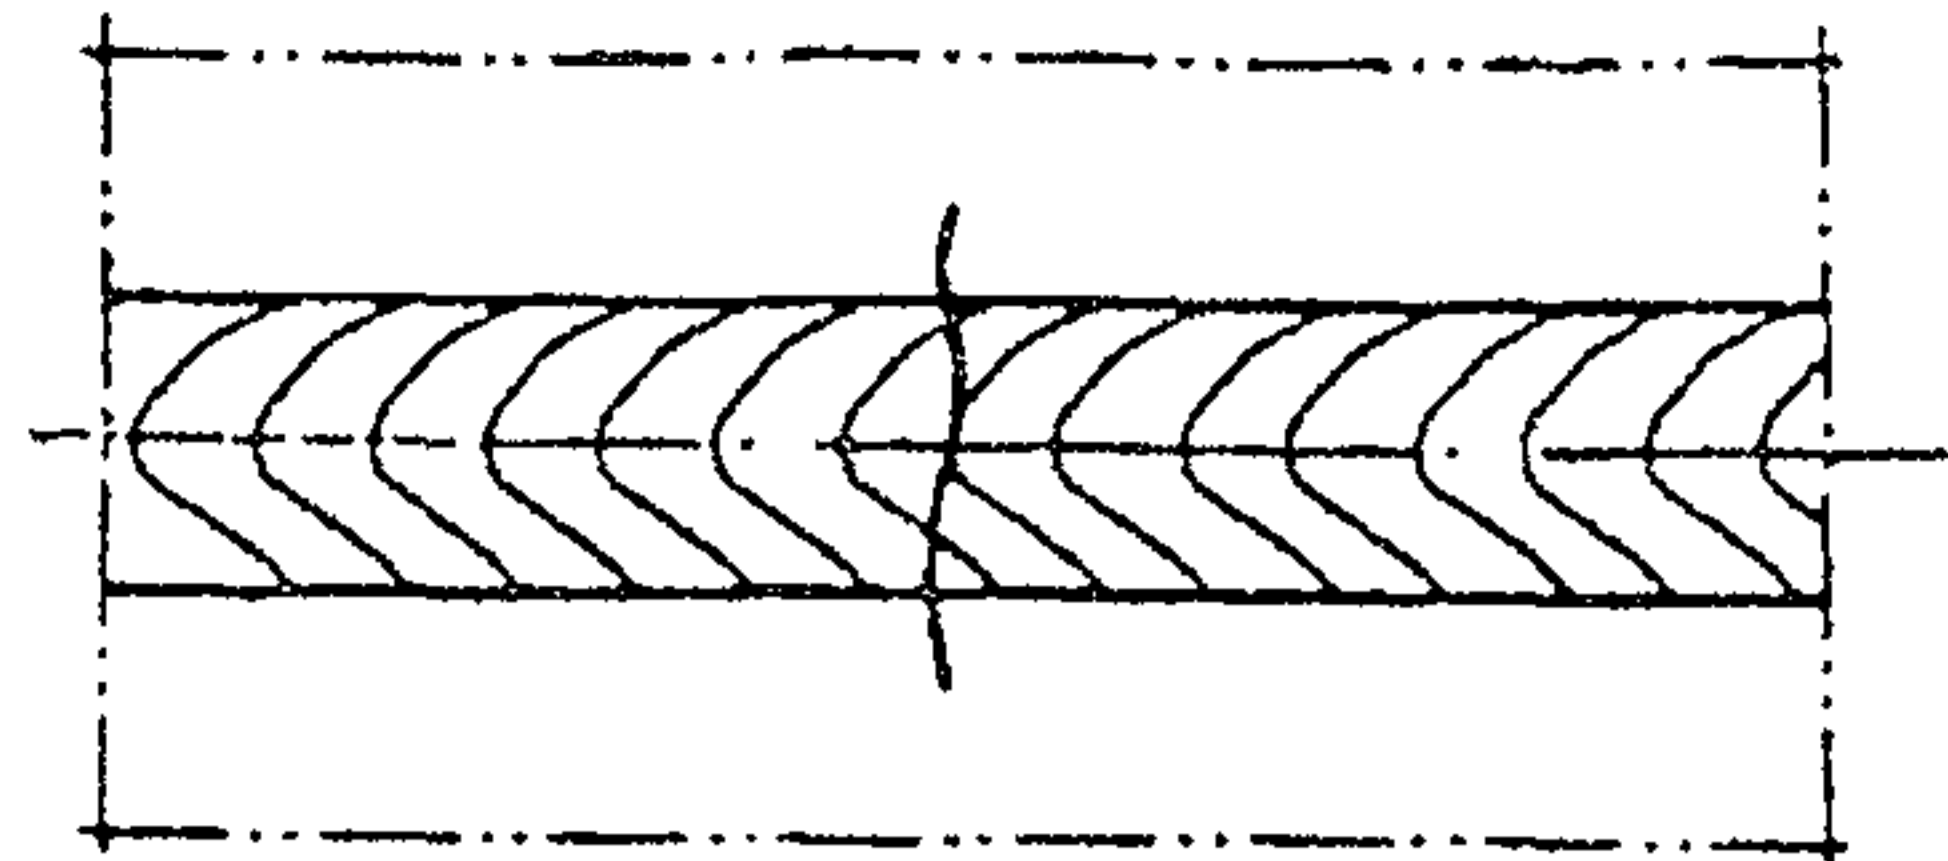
Поперечные трещины сварного соединения
